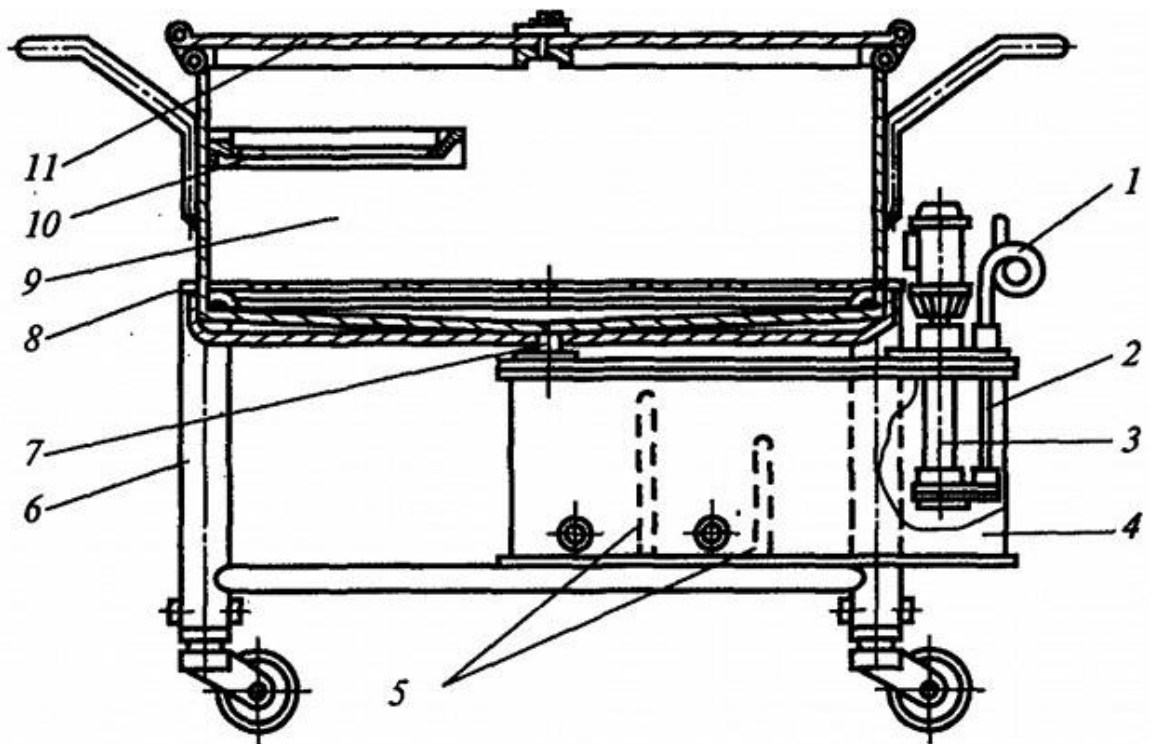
Передвижная моечная машина: 1 — шланг; 2 — труба; 3 — электронасос; 4 — бачок; 5 — перегородки; 6 — тележка; 7 — патрубок; 8 — сетка; 9 — ванна; 10 — полка; 11 — крышка
